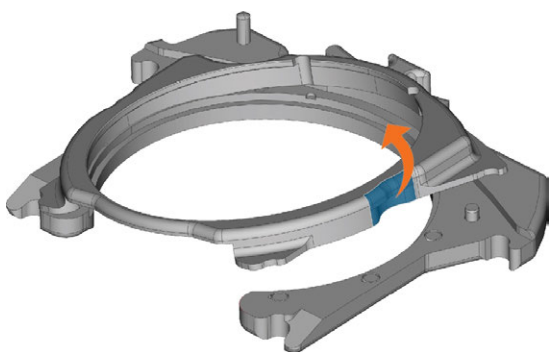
DÉMONTAGE DU COUVERCLE DU CADRE DE PIÈCES BRUTES
